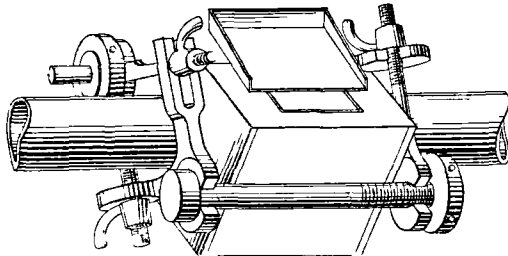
Moule avec plaque protectrice pour soudure de deux tuyaux par l'aluminothermie.
